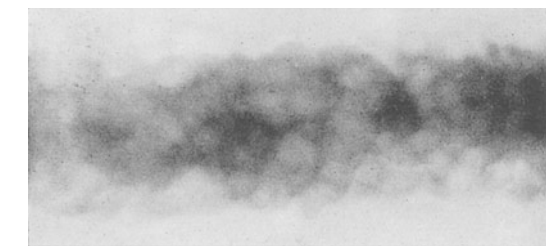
Röntgenbild einer guten Aluminiumblechschweißung (gehämmert).
